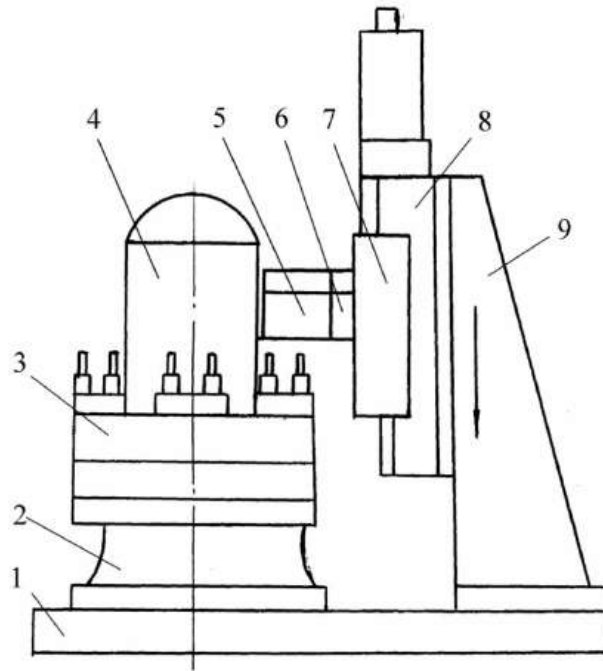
Модуль вертикального компонування для багатшпindelної обробки
